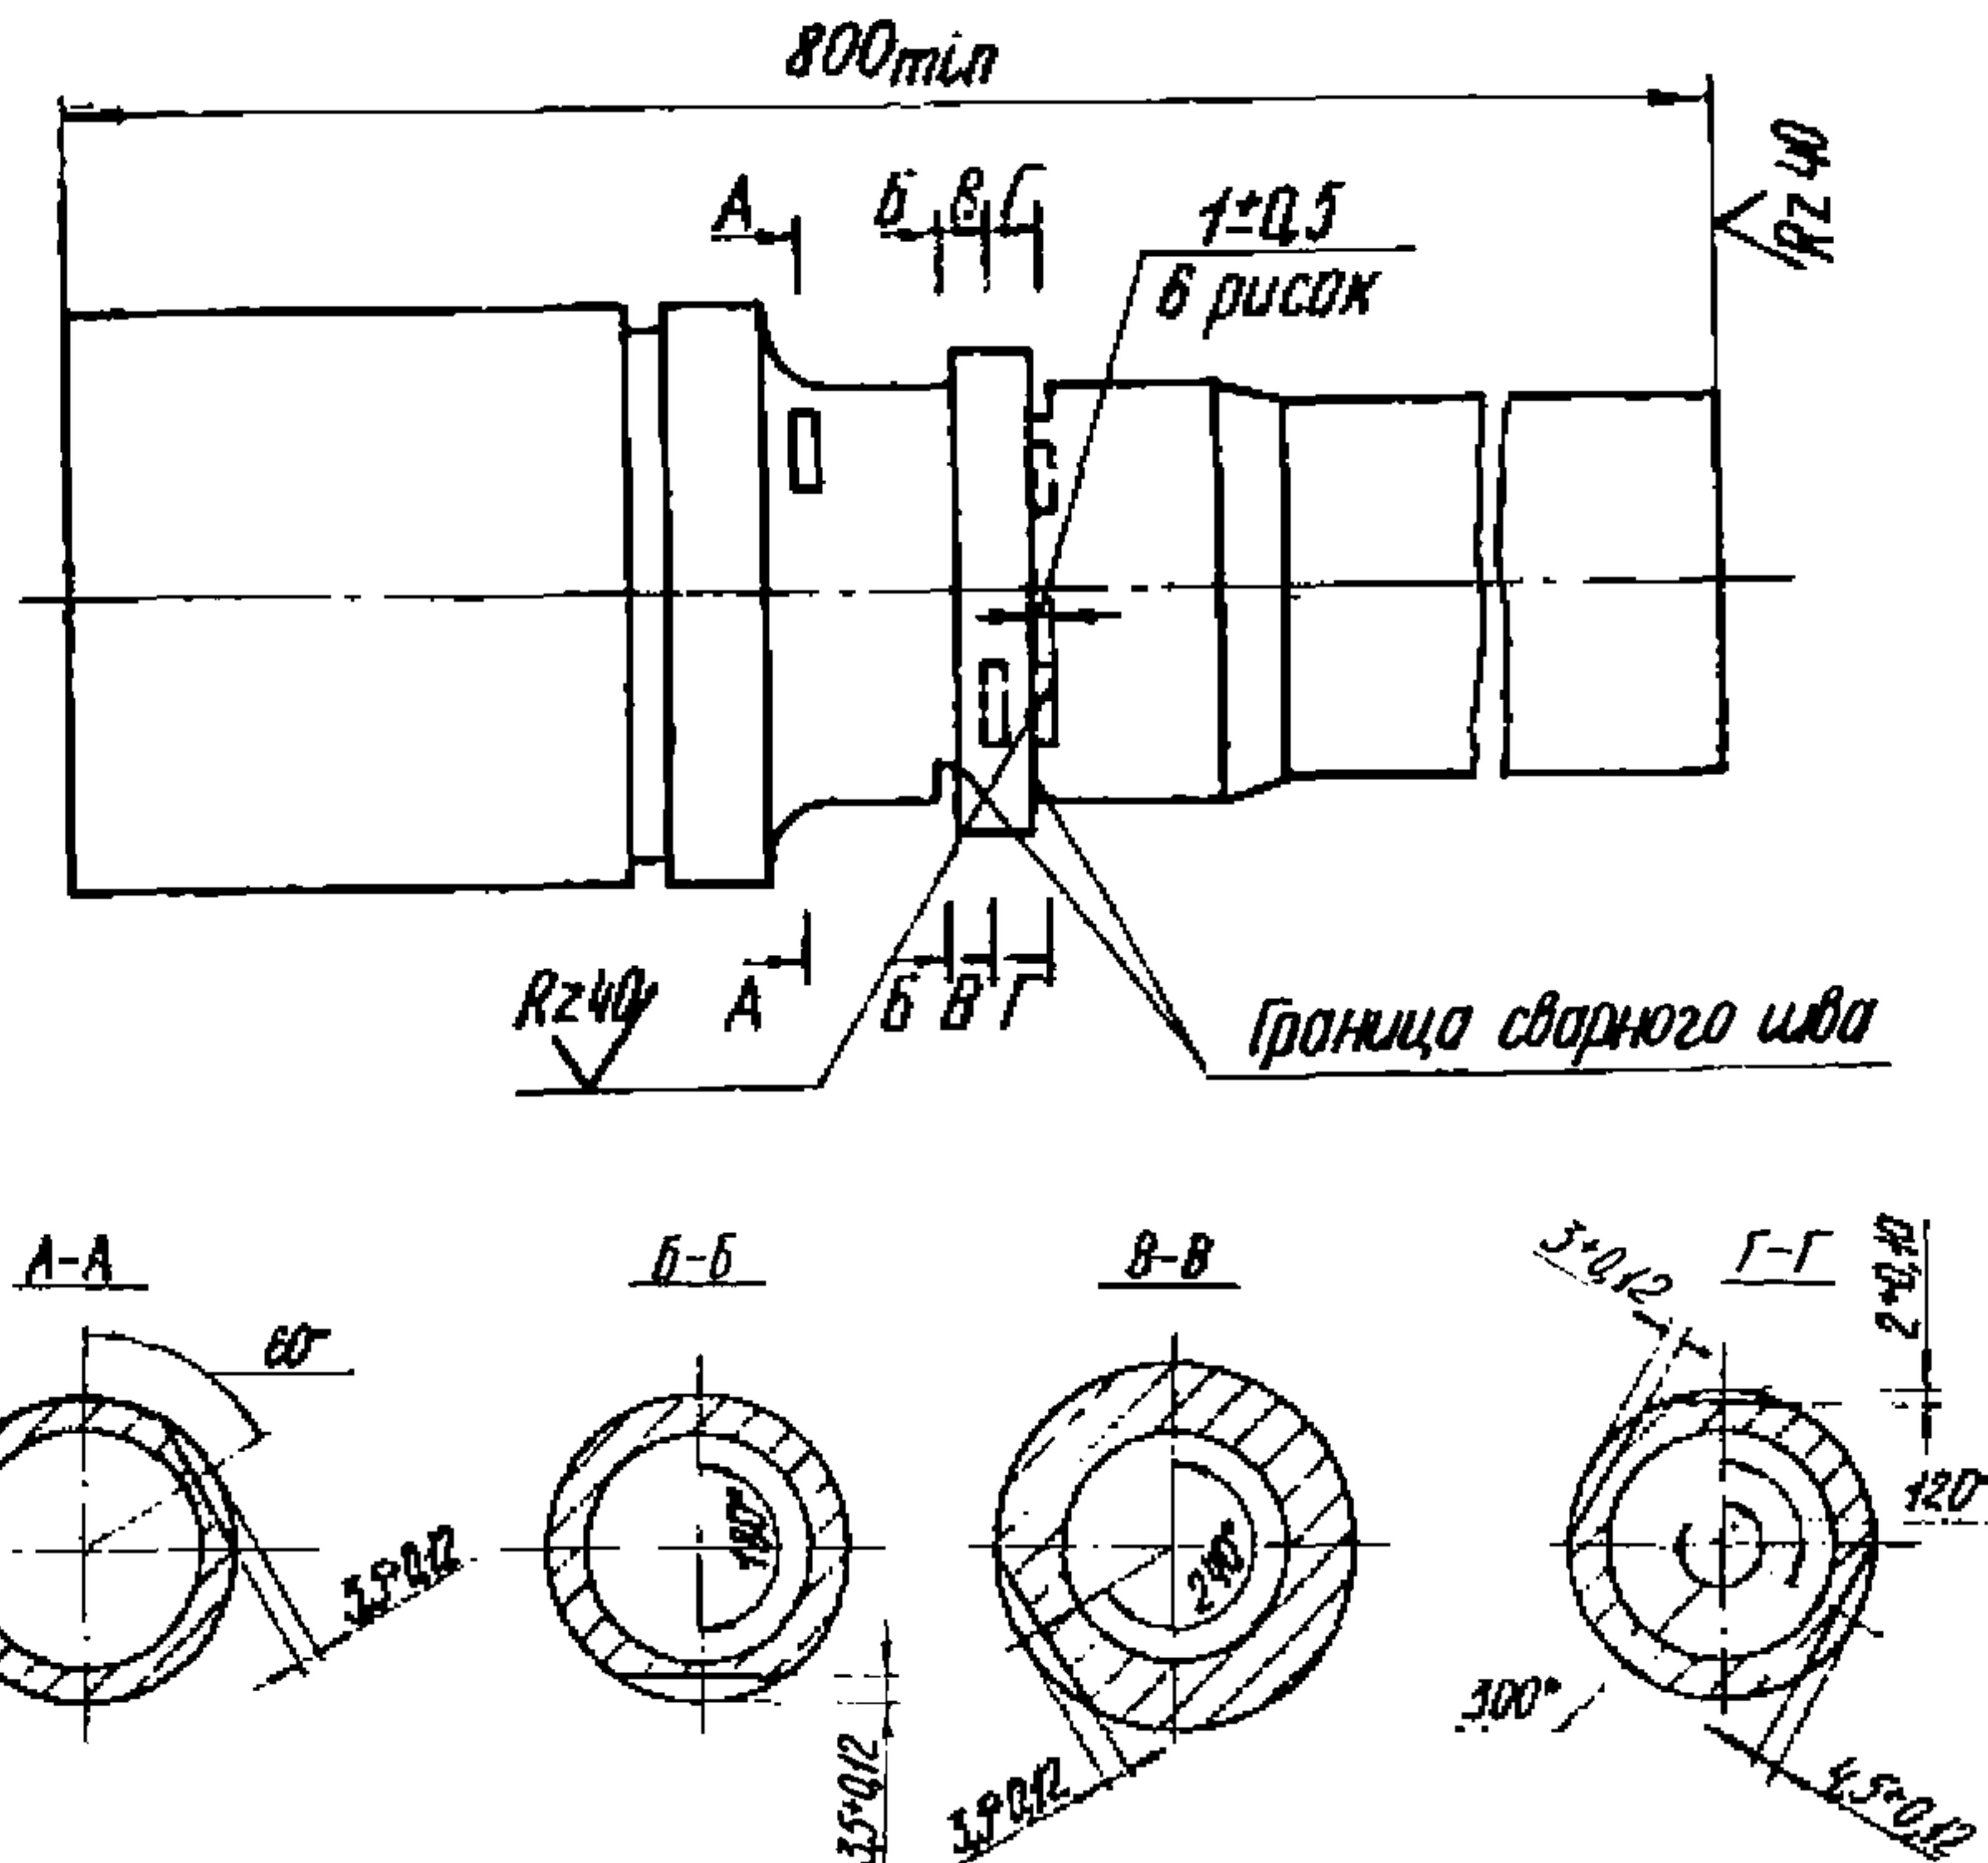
Испытательный образец для настройки дефектоскопа при контроле зоны сварного шва труб ТБПВ
